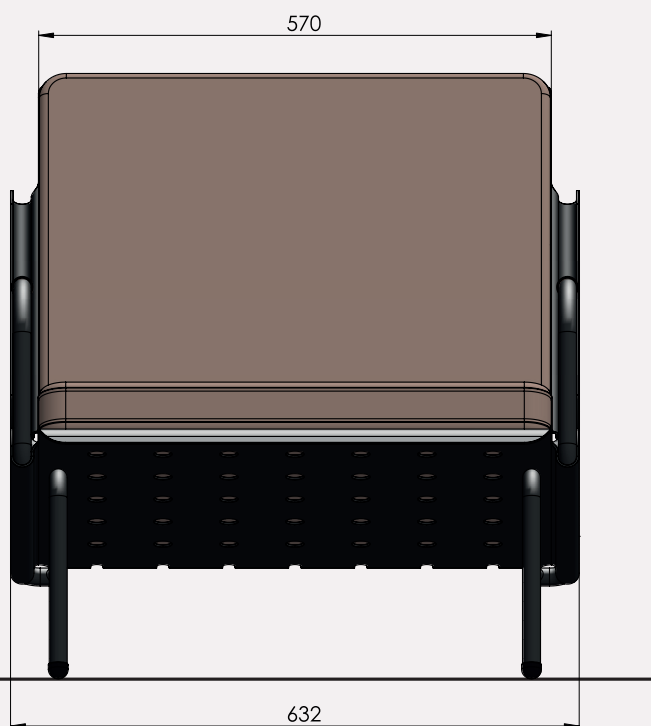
Målsatt tegning med endelige vinkler og dimensjoner sett fra siden. Alle lengder er målt i millimeter.
